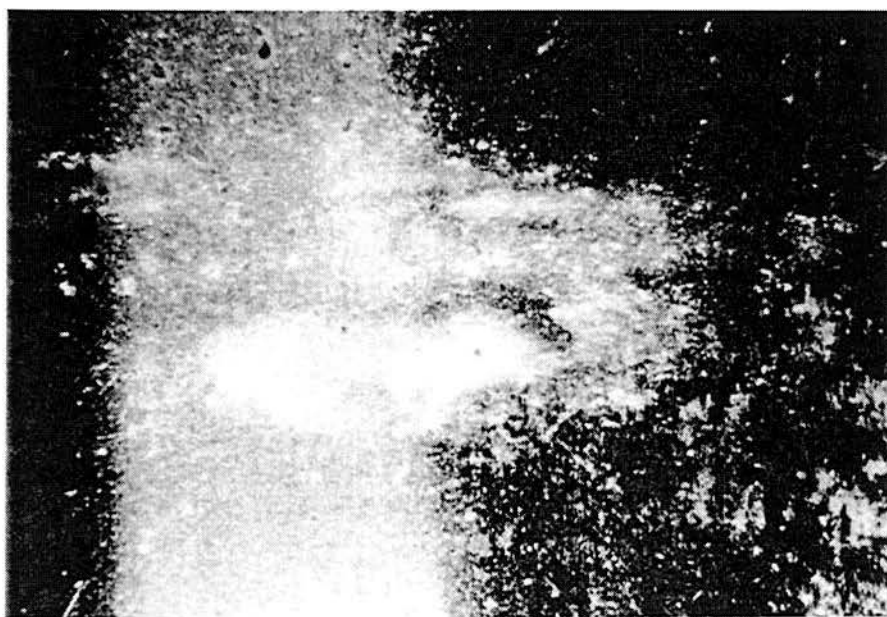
48MVT01D - Pista externa LA, outro detalhe
